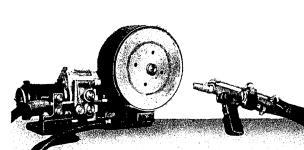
Подавающий механизм и сварочная головка полуавтомата ПДША-500
